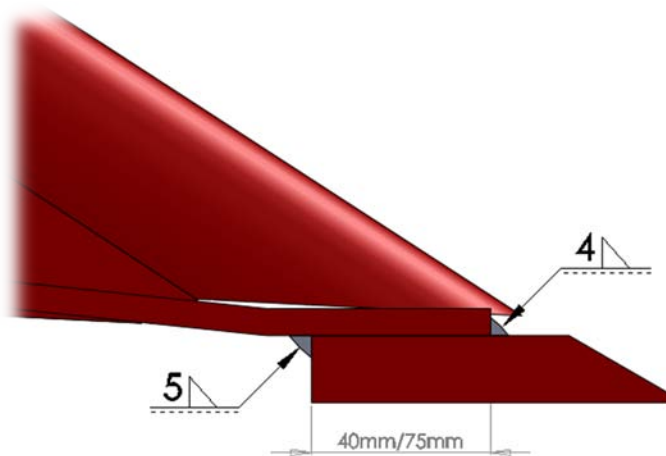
Chevauchement de la lame et du godet hydraulique
